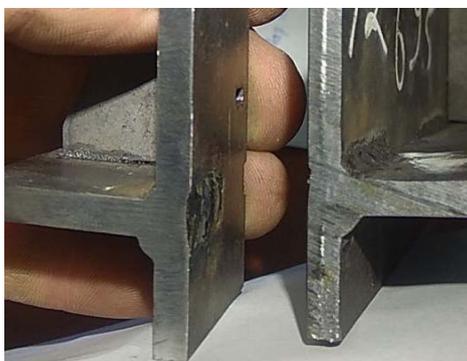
Шлиф сварного шва, толщина сваренных деталей 5 мм.
